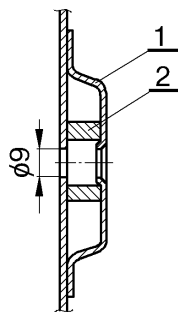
Установка распорной втулки в полость усилителя щитка передка.
